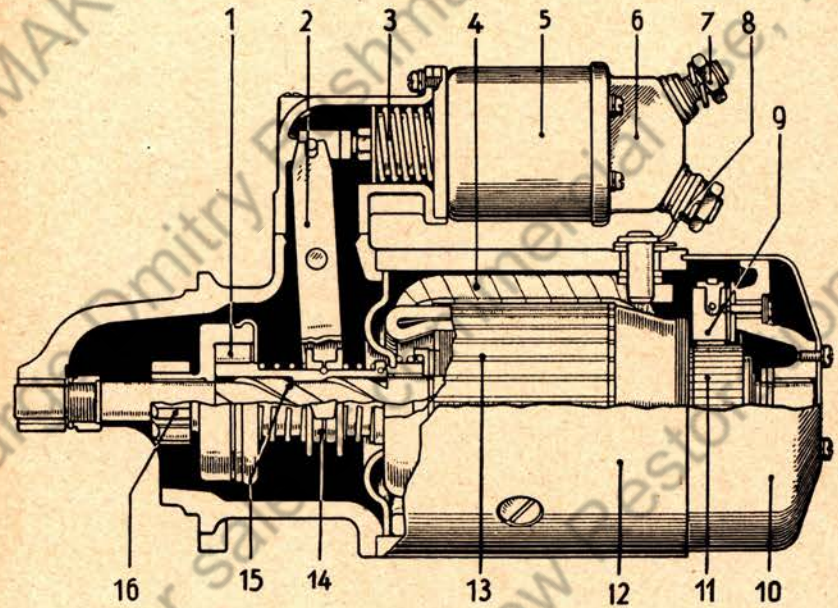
Schubschraubtrieb-Anlasser (aufgeschnitten)
